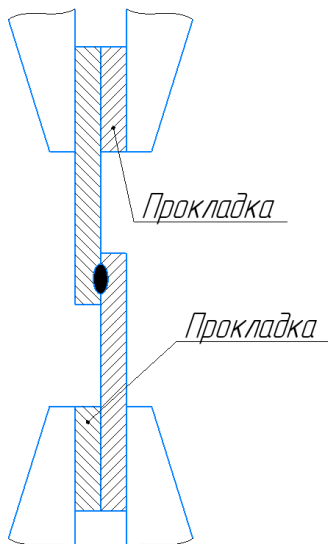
Схема зразка з однією зварною з'єднанням
